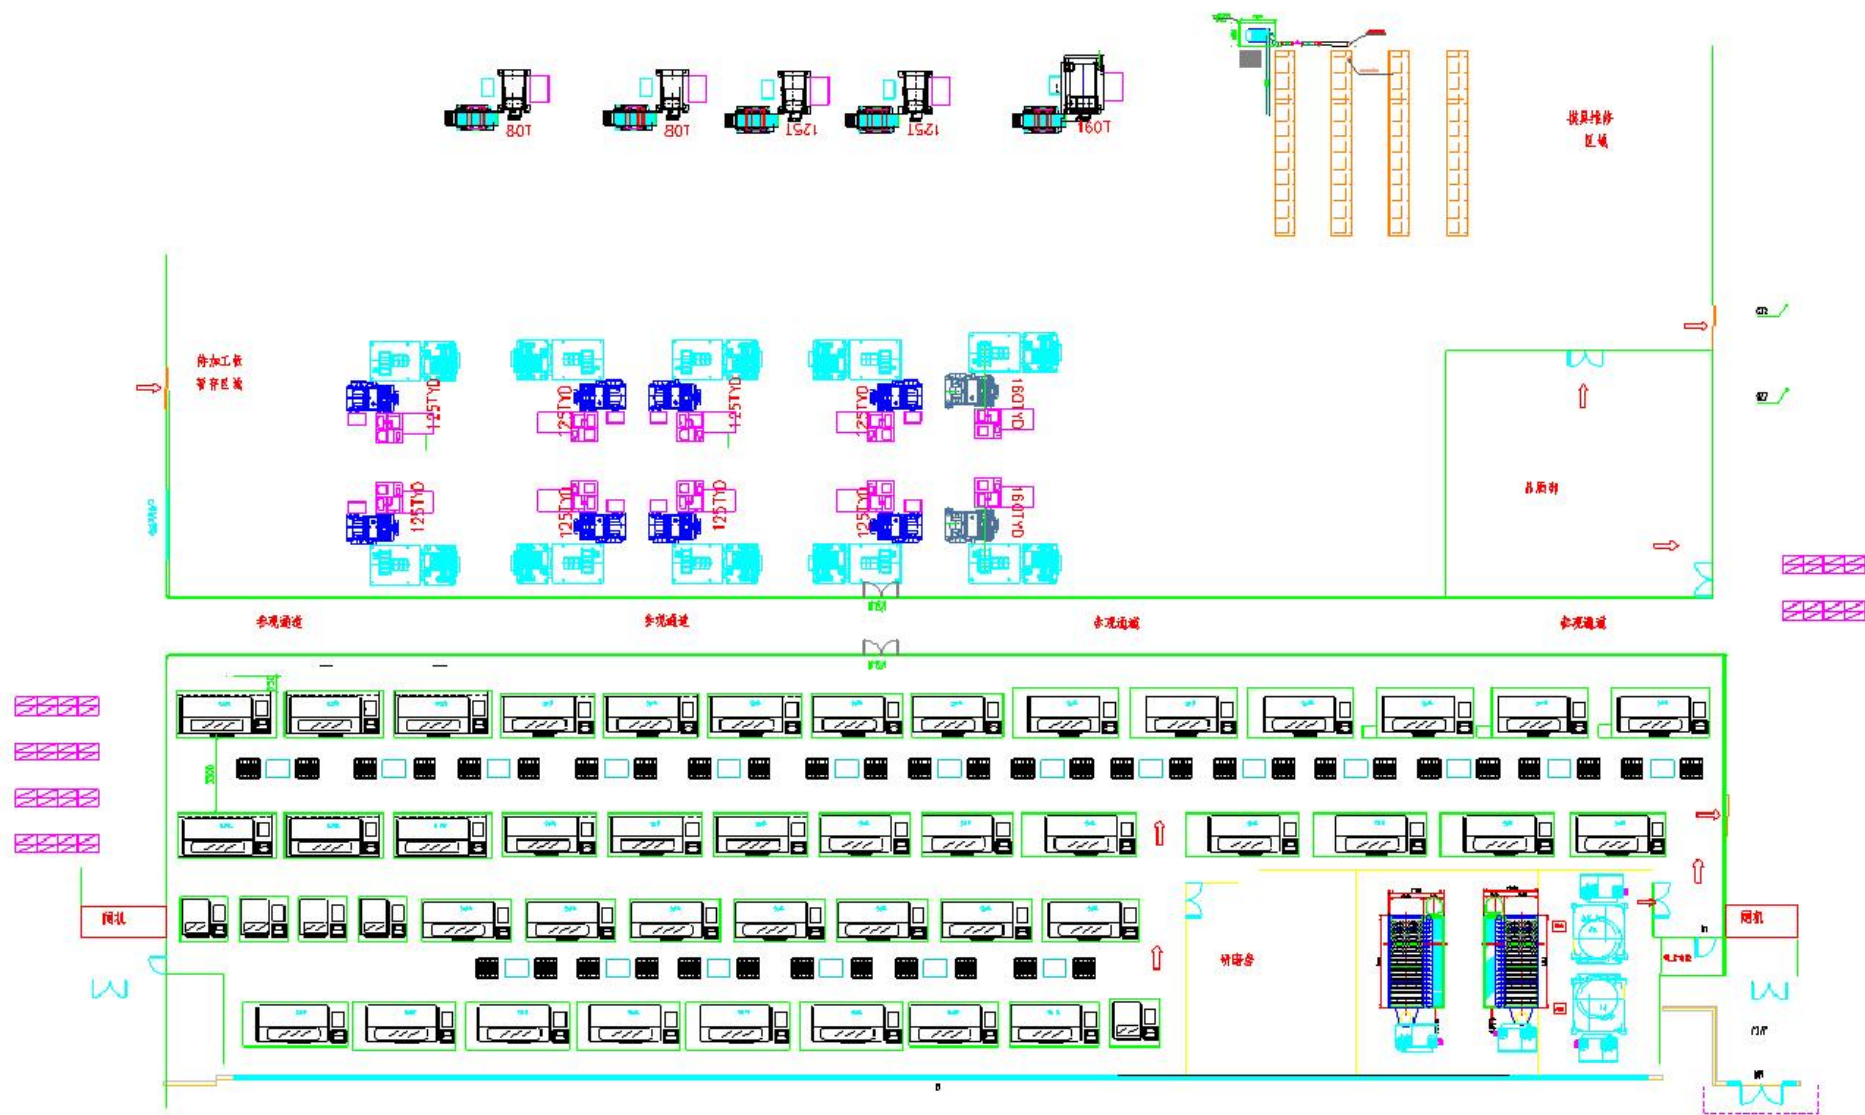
本项目二号厂房 1 楼实际平面布置图
